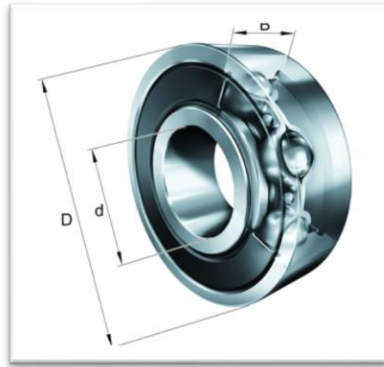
Rodamiento bolas SCHAEFFLER dimensiones principales
